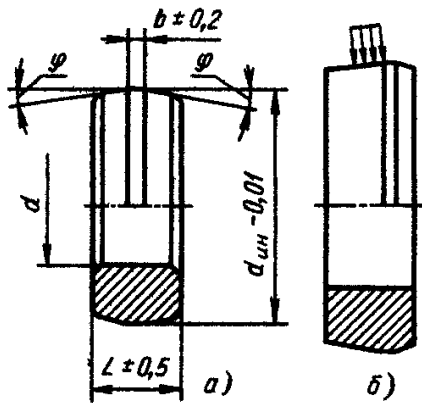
Деформирующий элемент сборной оправки: а — симметричный; б — симметрично-нагруженный
